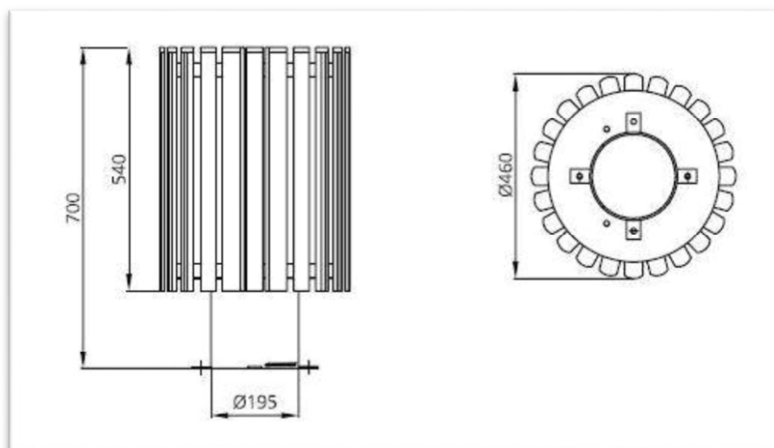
Características técnicas (cotas en mm). Fuente: Fundició Dúctil Benito
